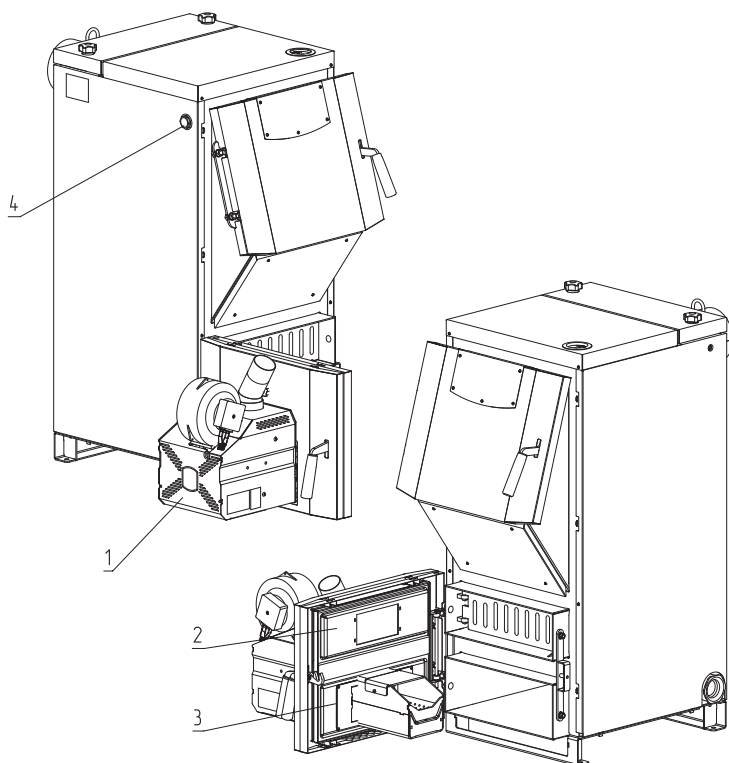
Порядок установки горелки ZOTA «RAY» на твердотопливные котлы ZOTA Bulat 18, 23, 28.
